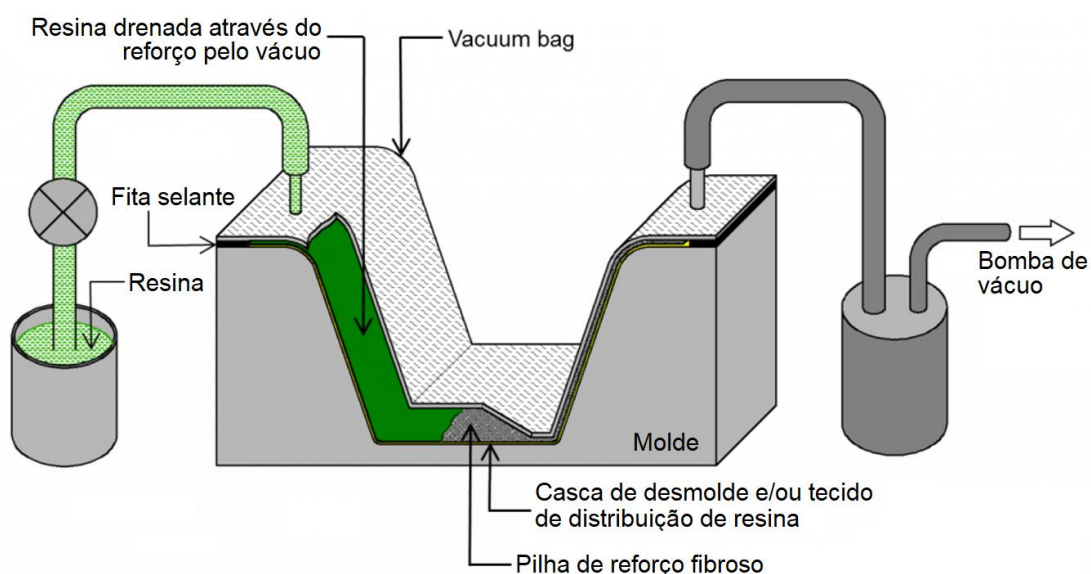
Processo *Vacuum Assisted Resin Transfer Moulding* (VARTM)
